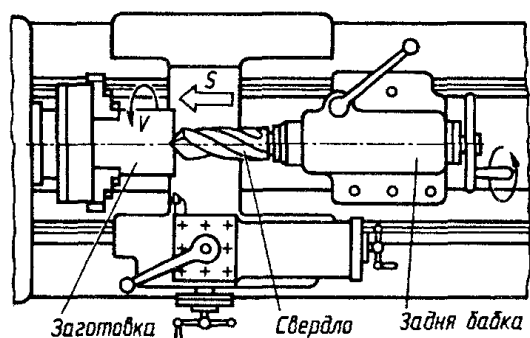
Свердління на токарному верстаті подачею вручну: 1- задня балка; 2 – свердло; 3 - заготовка
